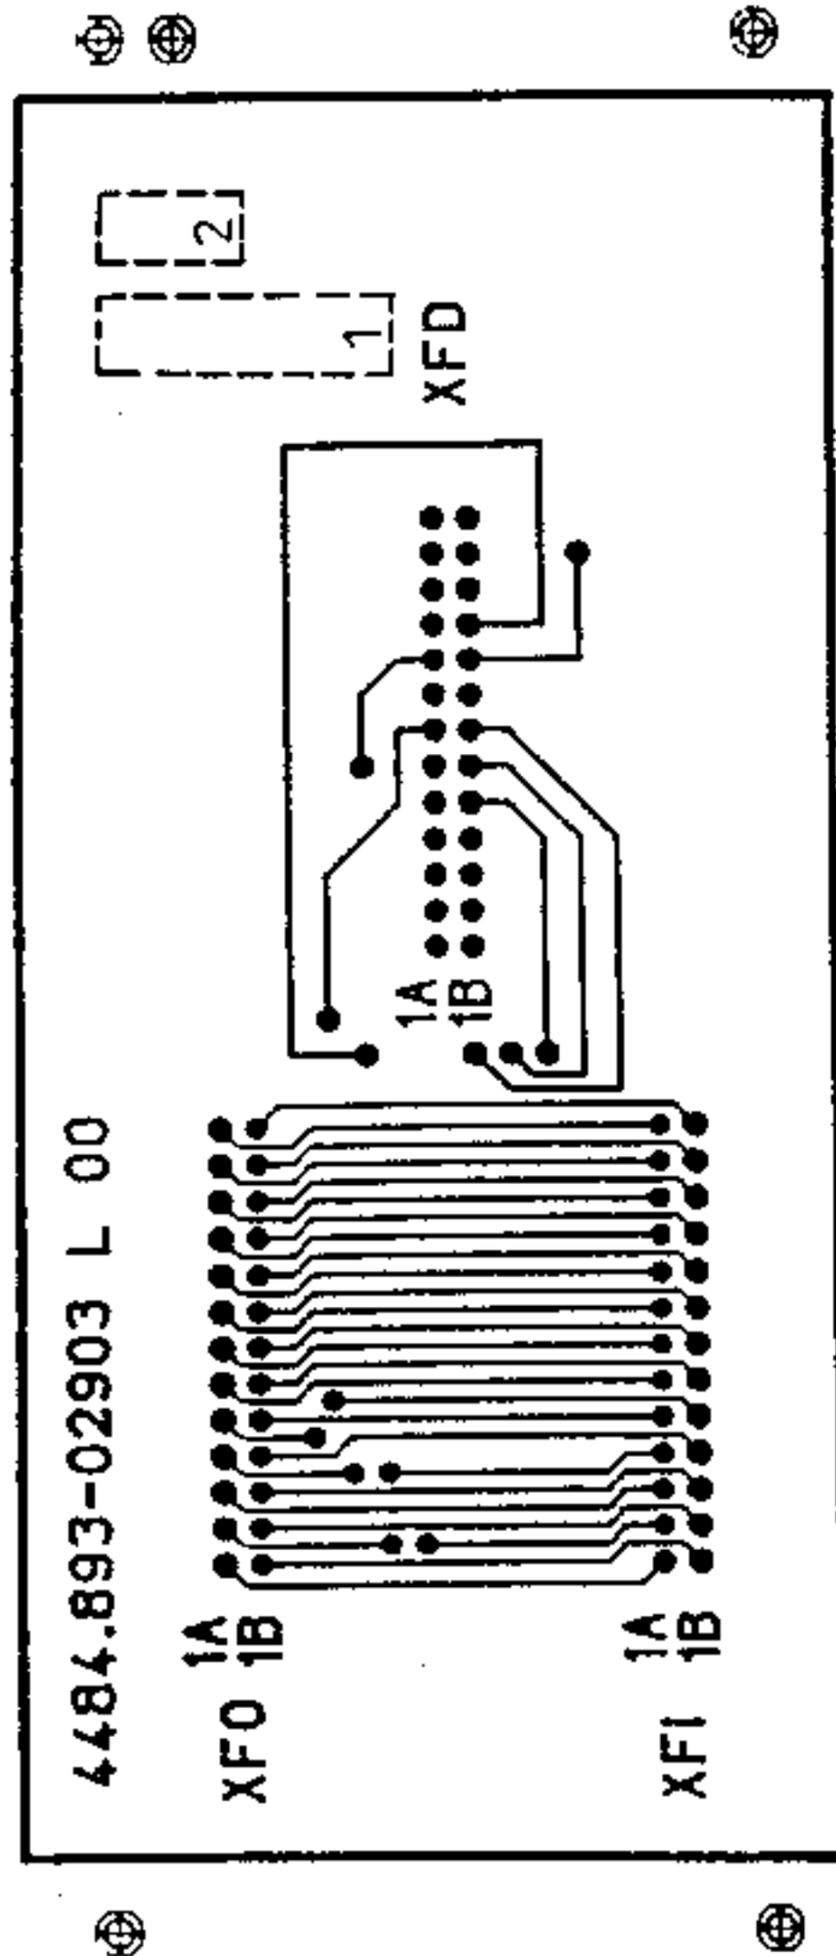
Leiterplatte gemäß Zeichnungs-Nr. 4484.893-02903
